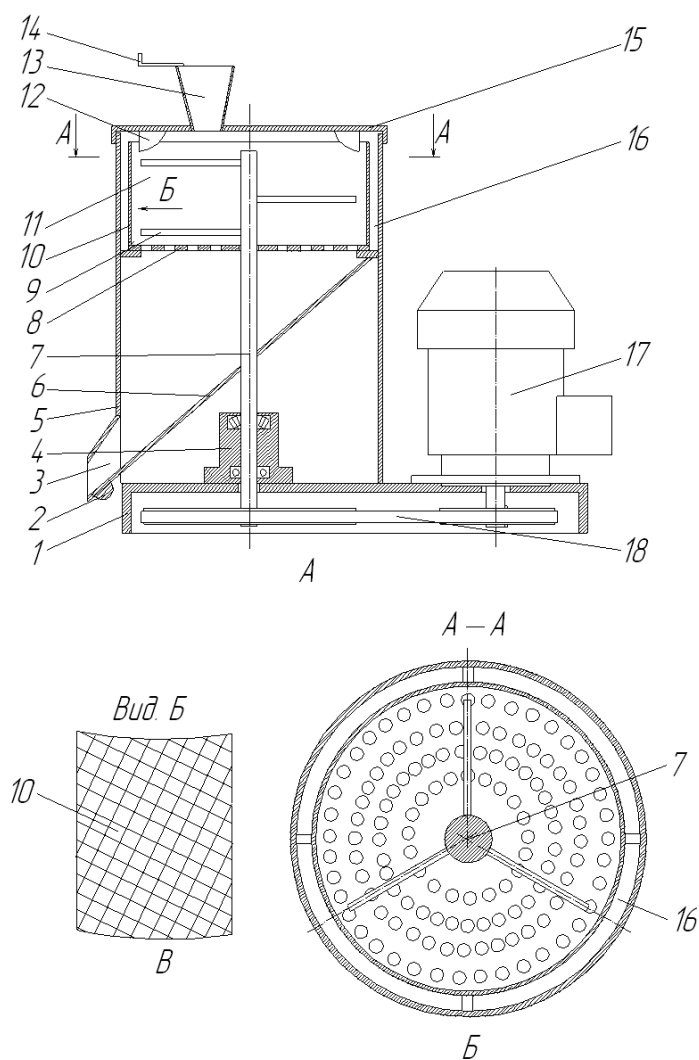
Схема измельчителя перговых сотов: А – общий вид; Б – разрез А-А рабочей камеры; В – вид Б внутренней стенки дополнительной камеры
